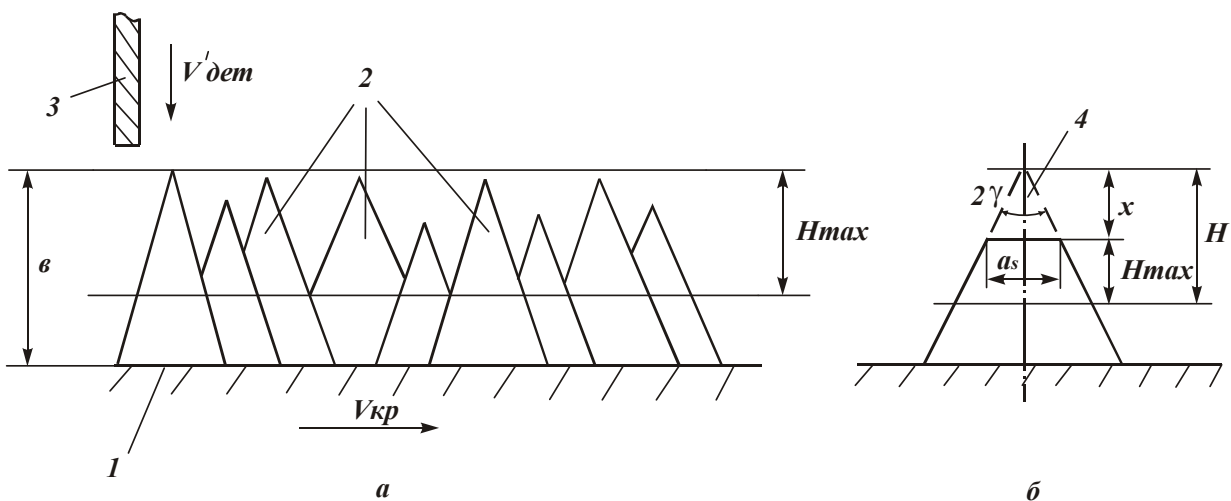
Расчетные схемы шлифования: 1 – связка круга; 2 – режущие зёрна; 3 – обрабатываемый образец; 4 – изношенная часть зерна.
